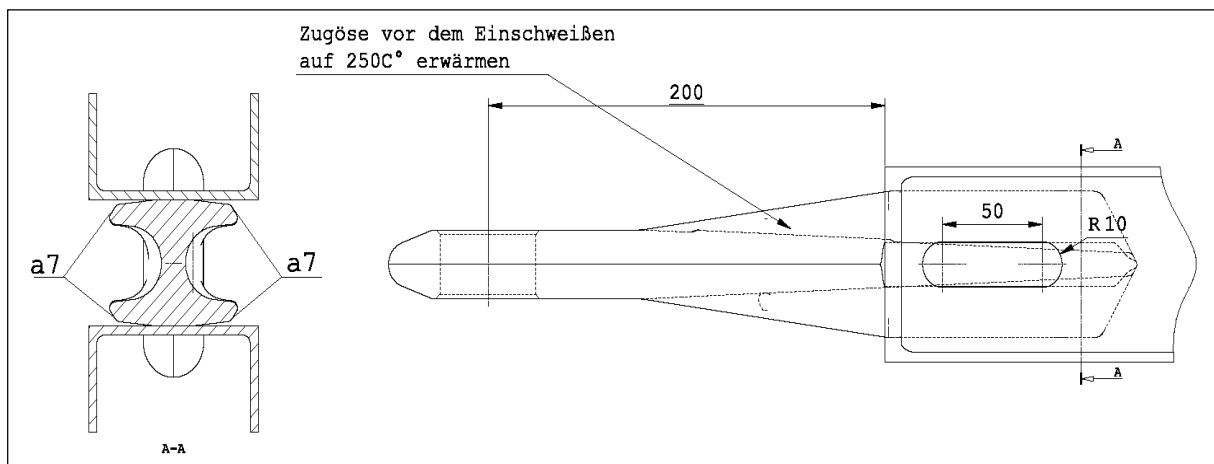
Exemplarischer Schweißnahtanschluss
